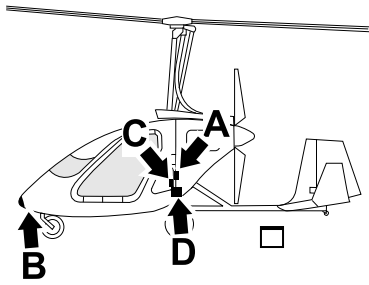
COMPONENTI ELETTRICI 1ª parte
